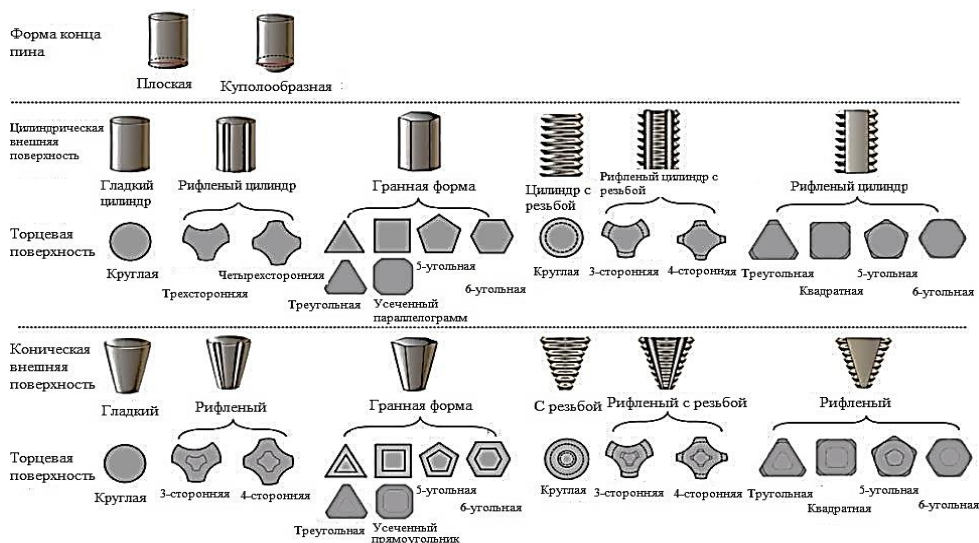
Классификация видов форм пина инструмента для сварки трением с перемешиванием
